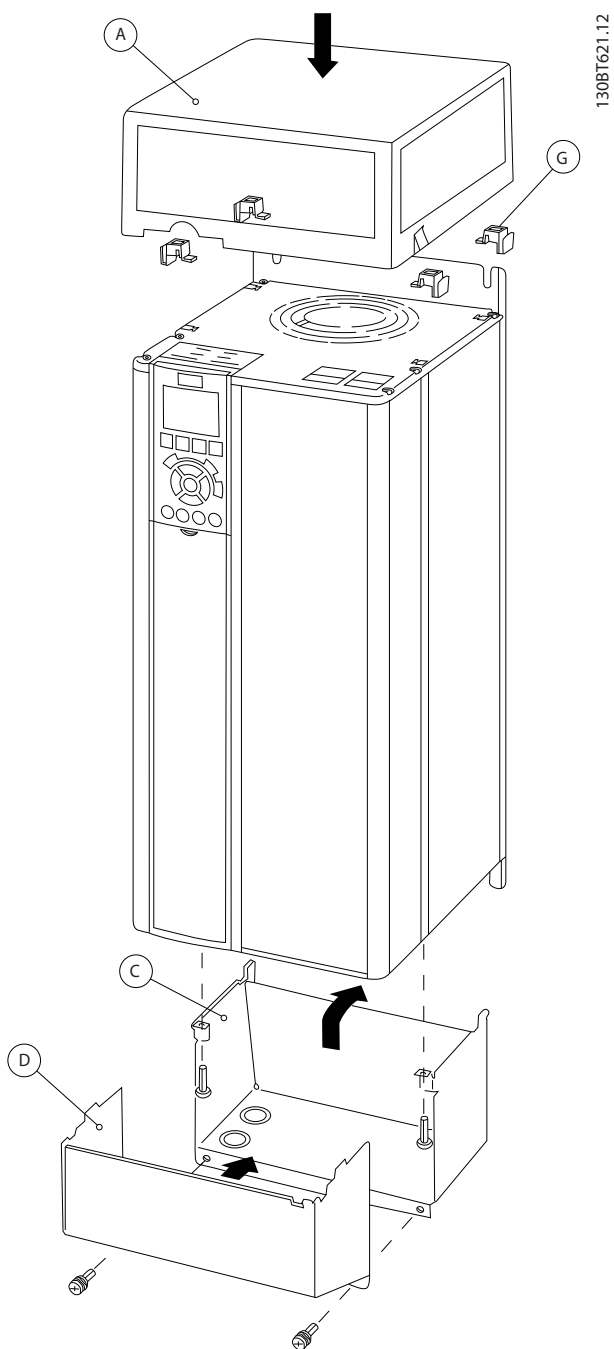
Gehäusetypen B4 - C3 - C4
